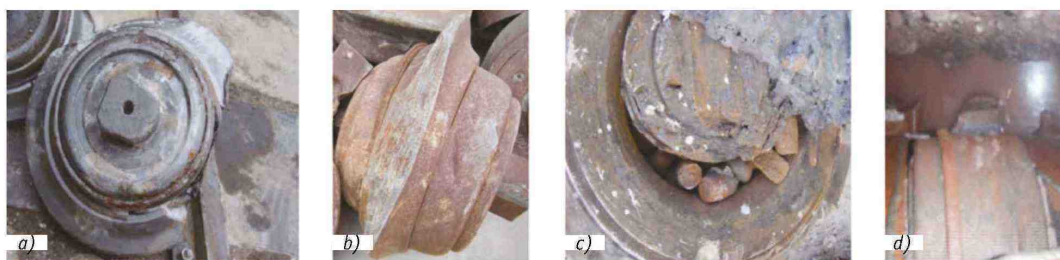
Виды повреждений резца: а) обломки кромки; б) неровный износ кромки; с) повреждение подшипника; d) осыпание фрезы
